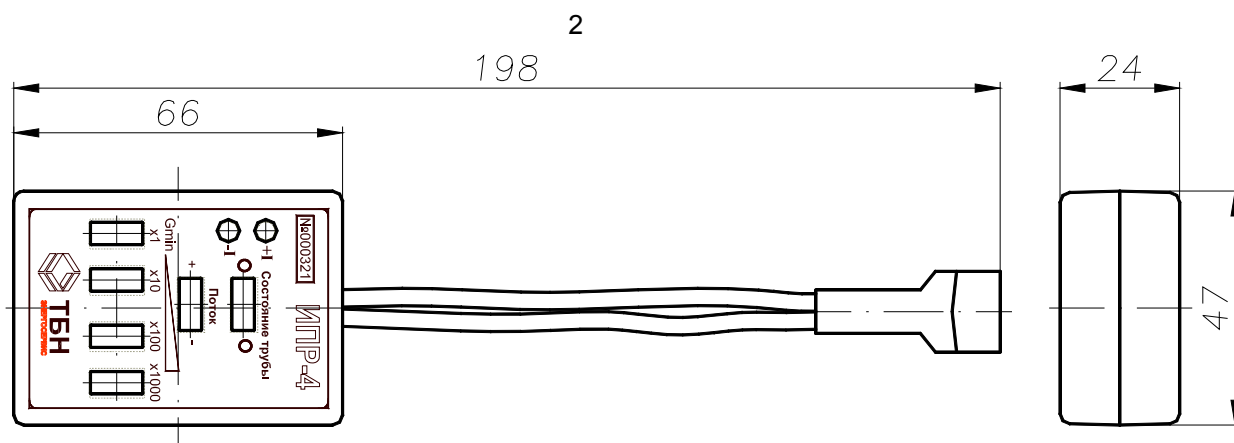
Внешний вид и габариты имитатора преобразователя расхода
